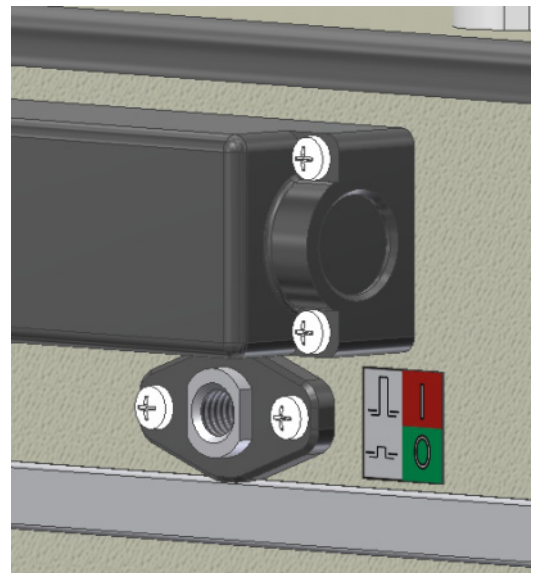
Присоединительные размеры блокировочных тяг и синхронизирующего вала ISM25_LD_1
